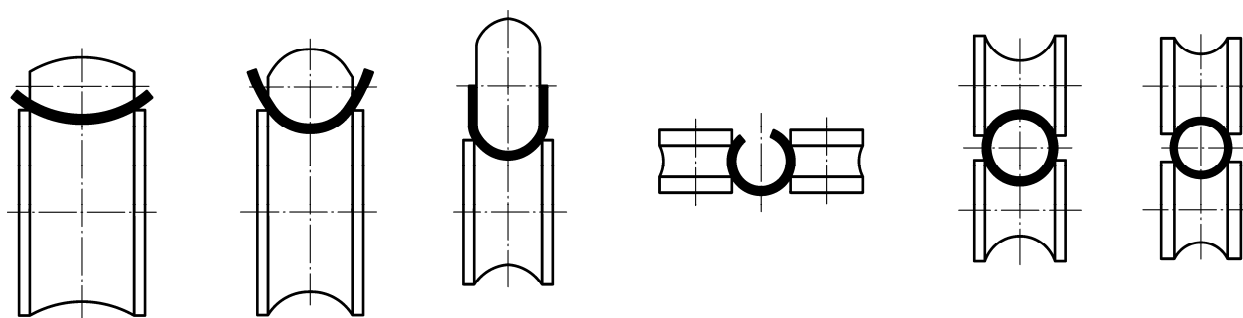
Последовательность процесса свертывания трубы из полосы в шести валках стана
